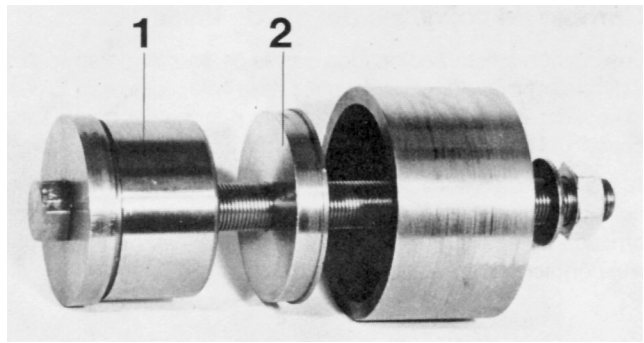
Outil 884489 pour démontage et montage des paliers de vilebrequin.
